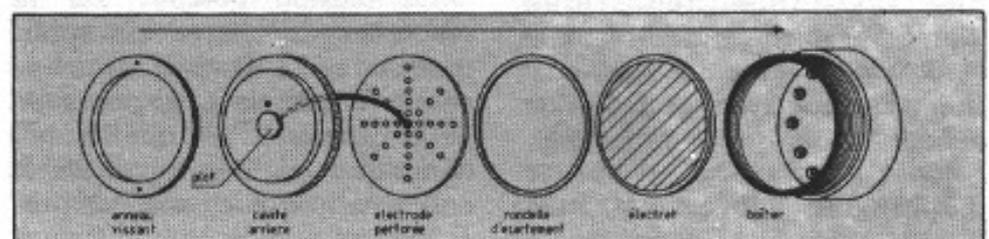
Vue éclatée de la capsule « EM23A ».
